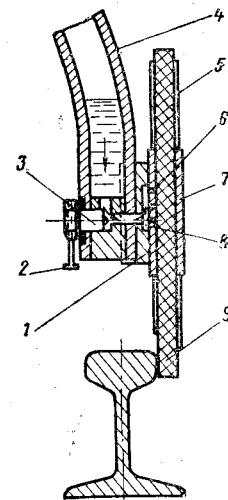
Рельсо-смазыватель конструкции Чекмарева, установленный на подвижном составе:
